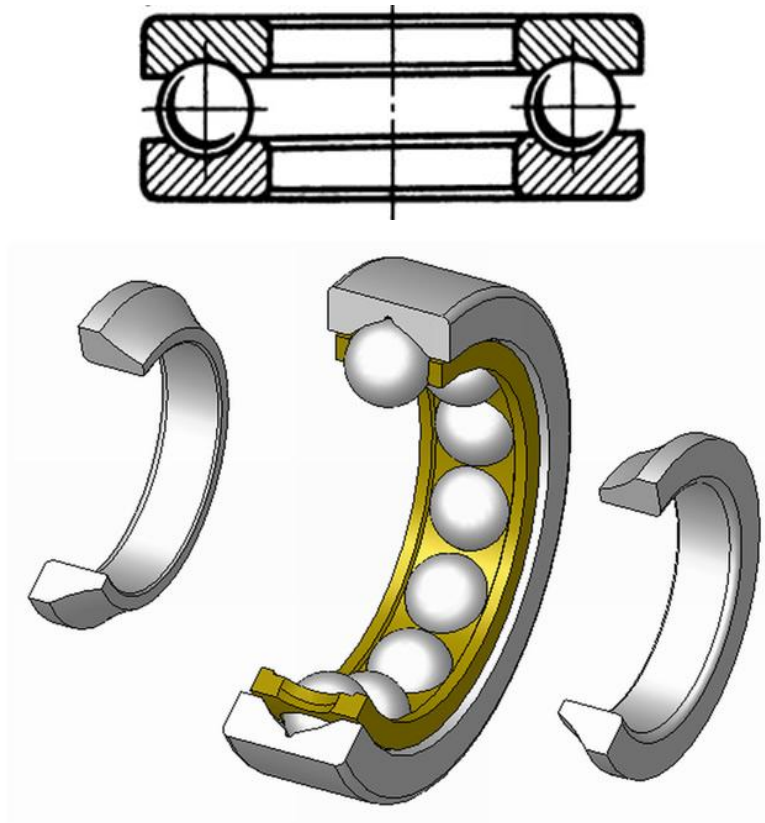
Упорний однорядний кульковий підшипник одинарний
